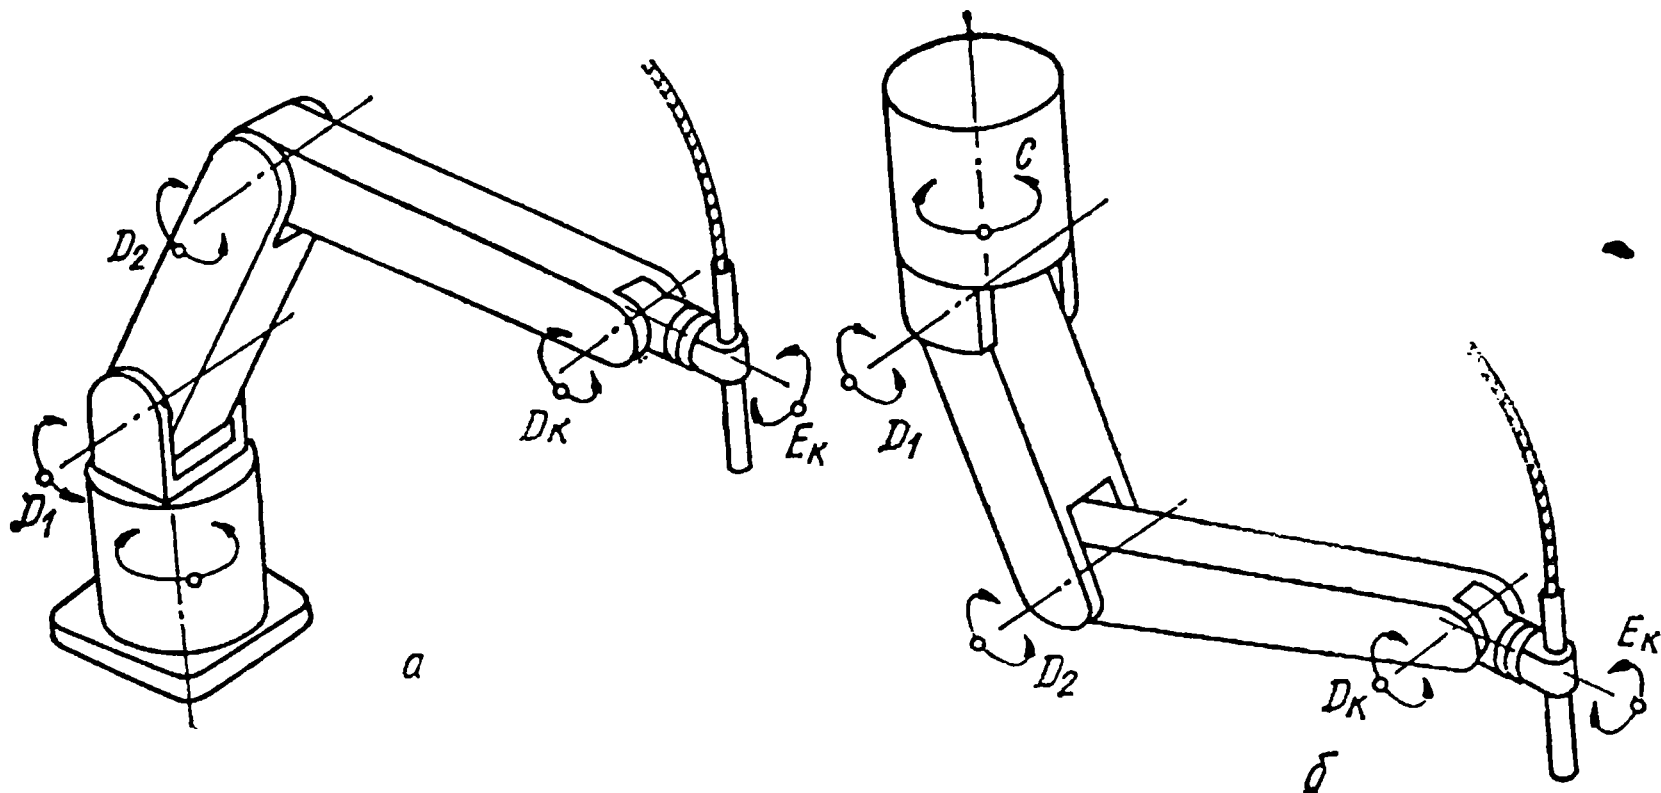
Компонентные схемы манипуляторов сварочного инструмента с двухполюсной сферической системой координат переносных движений:
